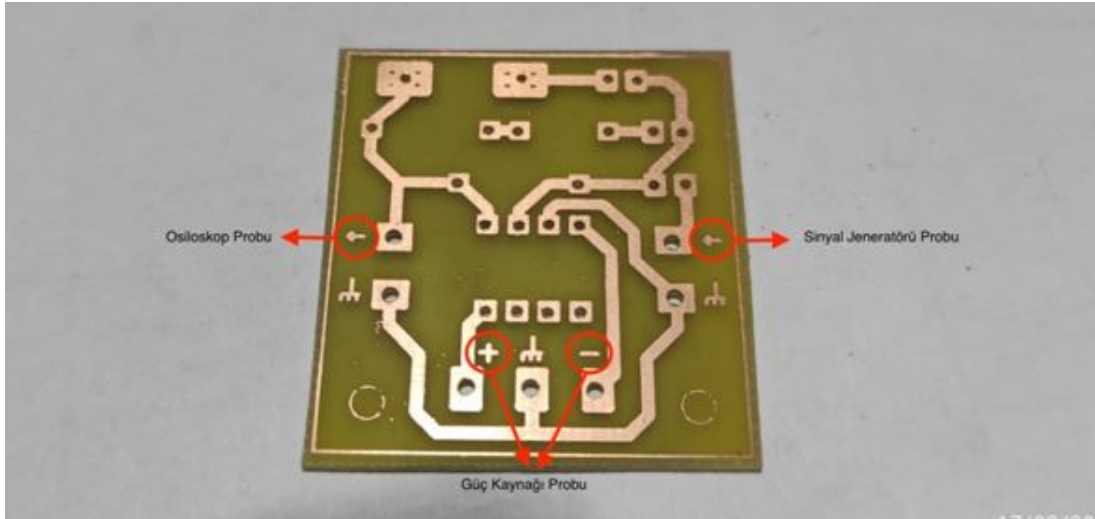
Tip 4 Devresinin PCB Kartı ve Komponentleri
